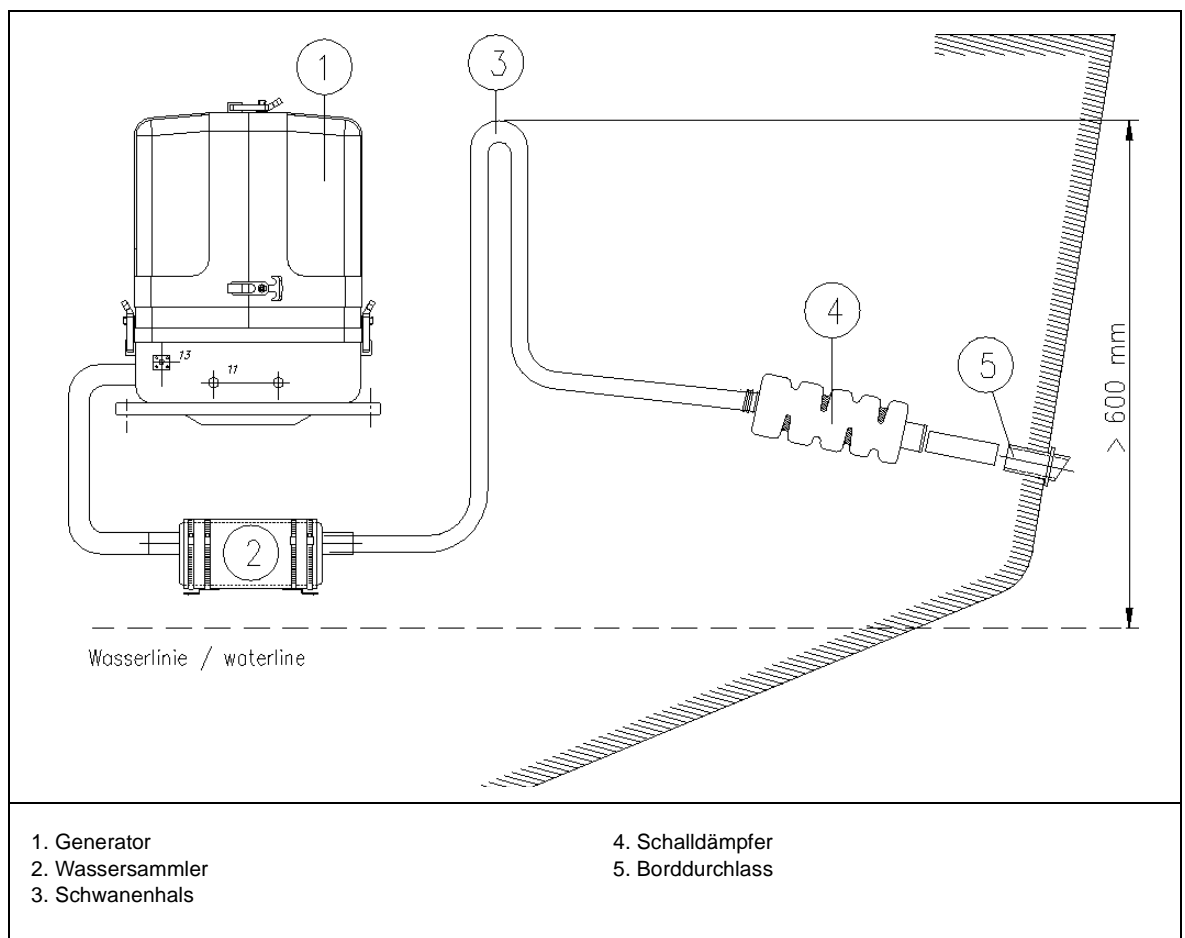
Installationsschema Standard-Abgassystem
